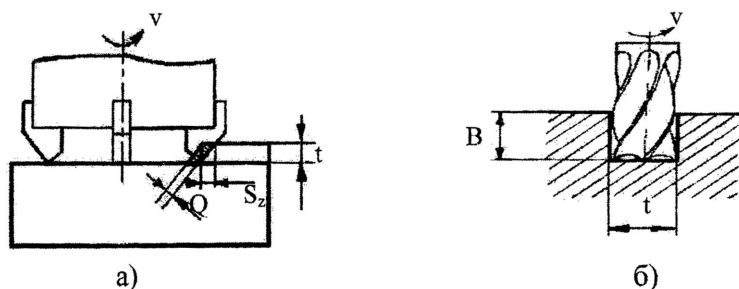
Элементы срезаемого слоя и режима резания при фрезеровании: а) поверхности торцевой фрезой; б) паза концевой фрезой
